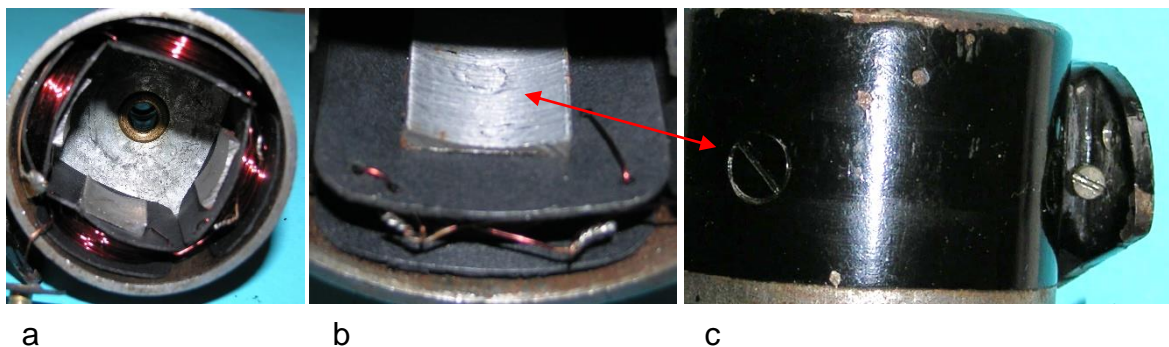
Angeschraubte Ankerpole: a) Vollständiger Anker, b) Überdrehte Polfläche mit der Schraubenmarkierung, c) Am Gehäusemantel sichtbarer Schraubenkopf
